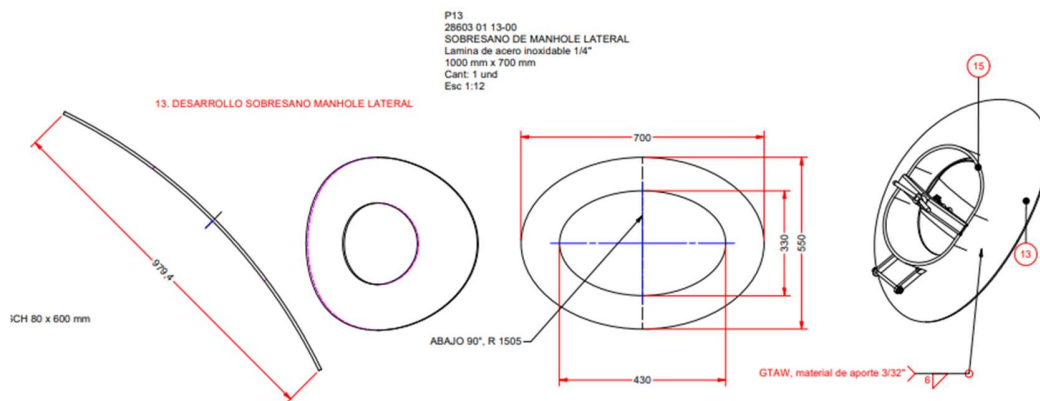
Desarrollo y soldadura de sobresano para manhole lateral ovalado.
